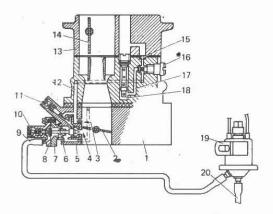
Esquema del sistema de ralentí del carburador 2107-1107010:
